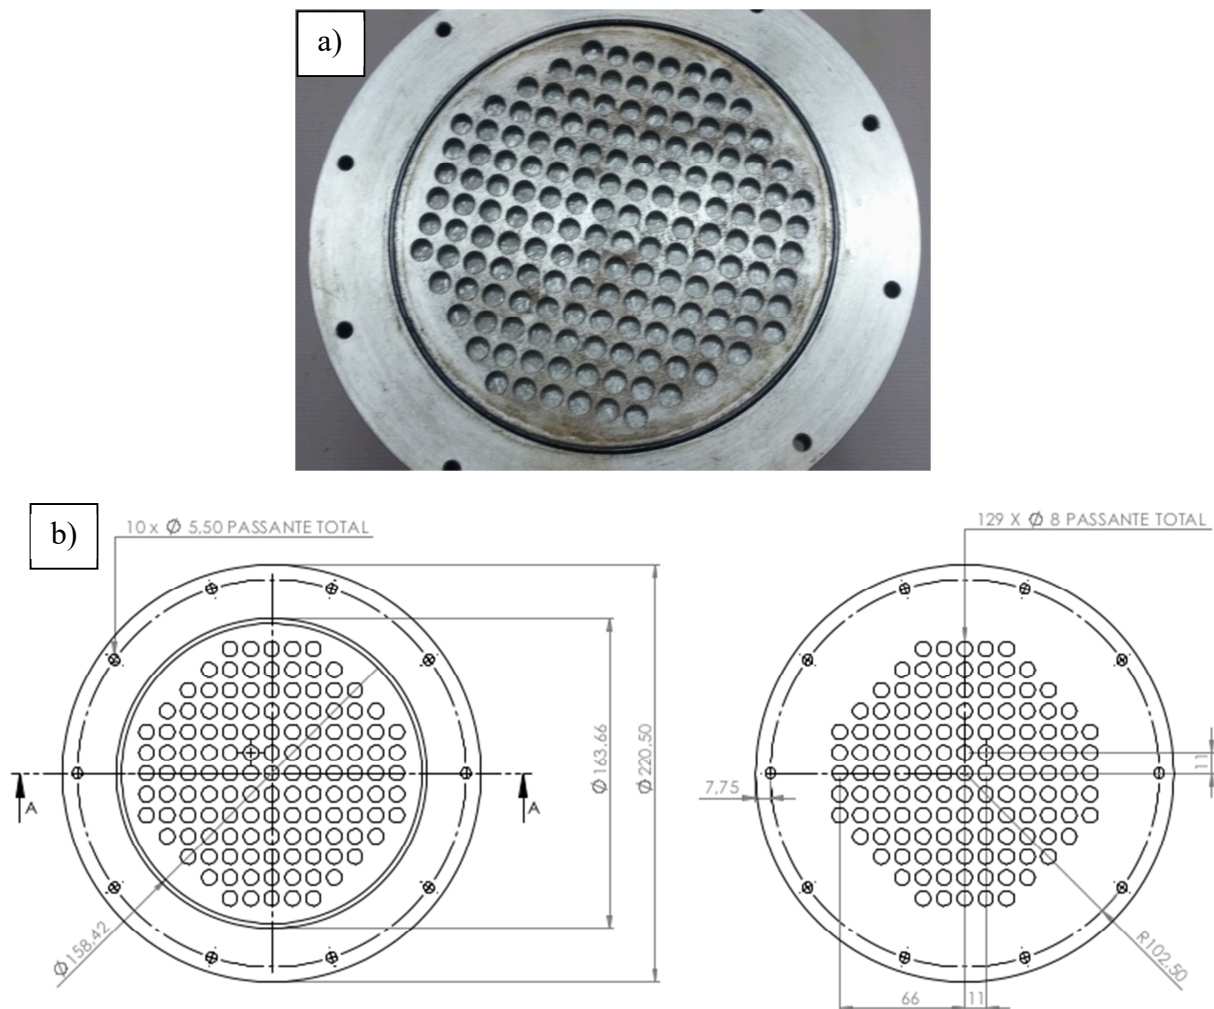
a) Placa perfurada usada no equipamento de medição de K_{zz} e b) Desenho técnico desta placa.
